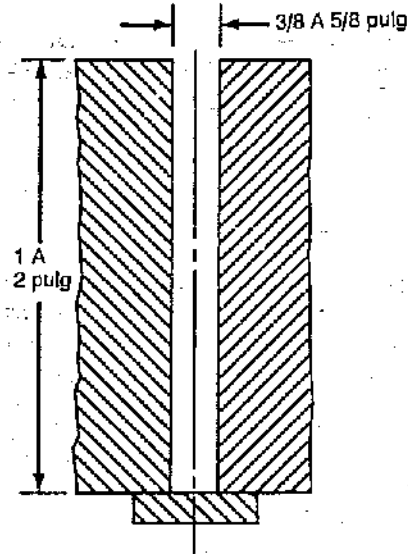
Configuración de unión típica para soldadura de separación angosta
